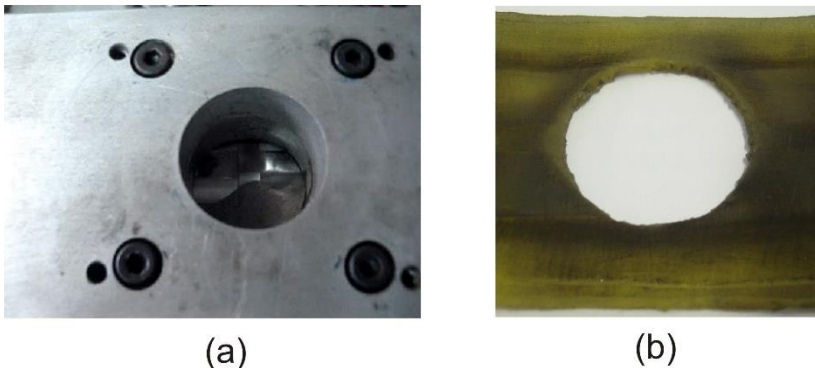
Válvula rotativa: a) vista superior durante manipulação de pó; b) superfície da vedação com partículas incrustadas
